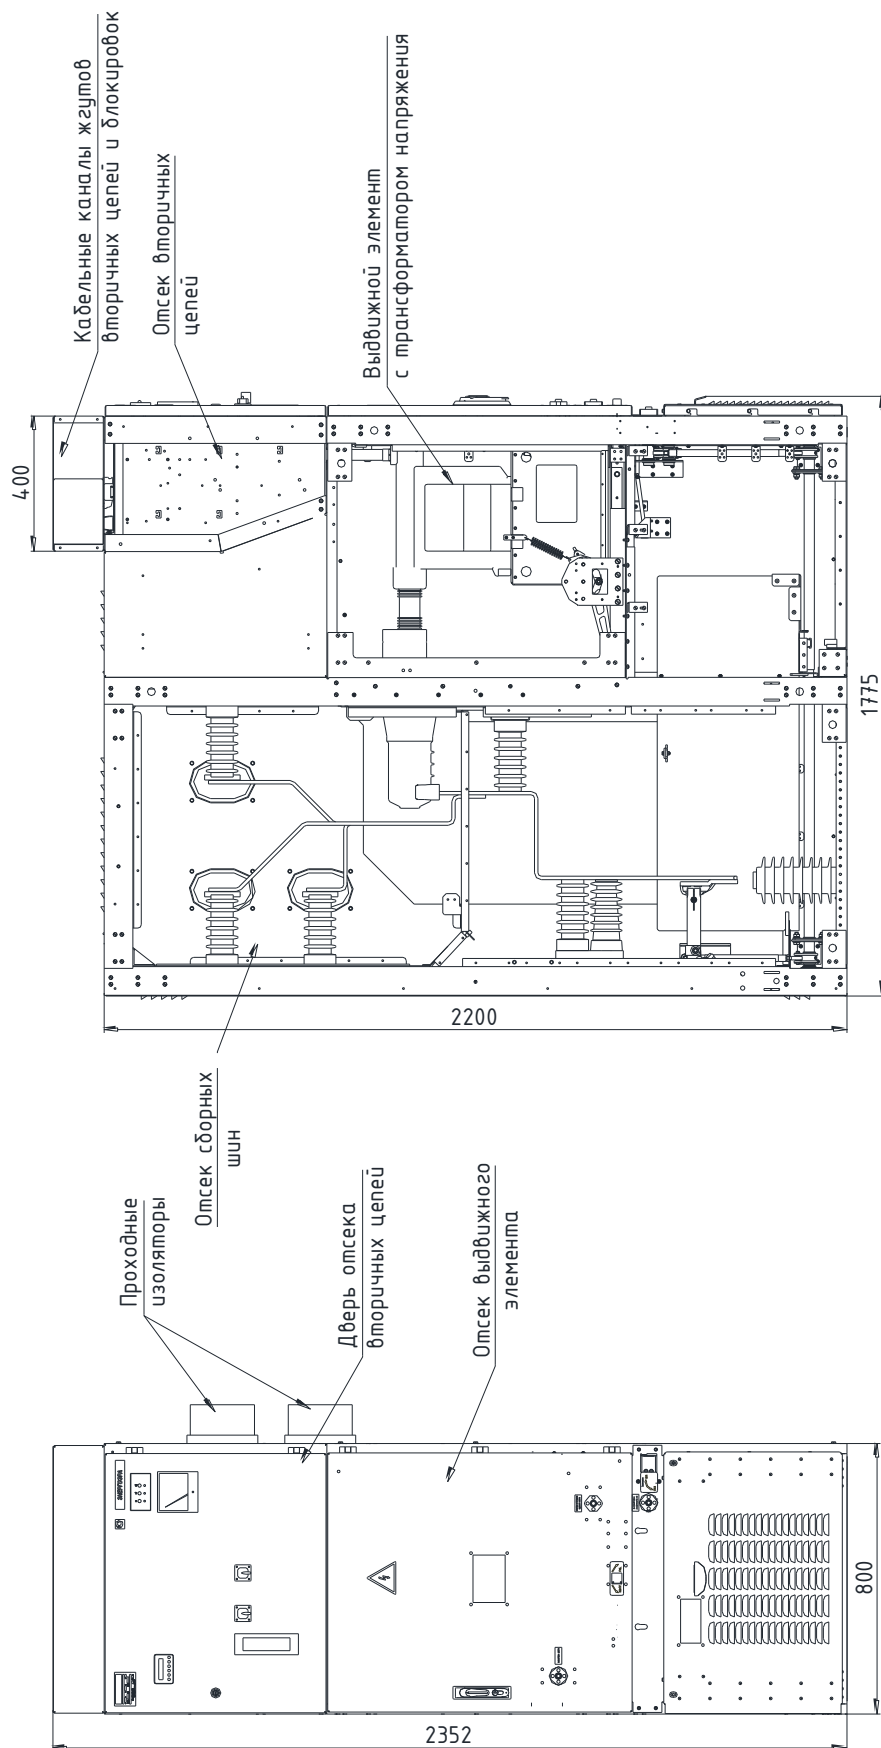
Габаритные размеры и компоновка шкафа КРУ «ОМЕГА-1» с ТН типа ЗНОПП-НТЗ-20
